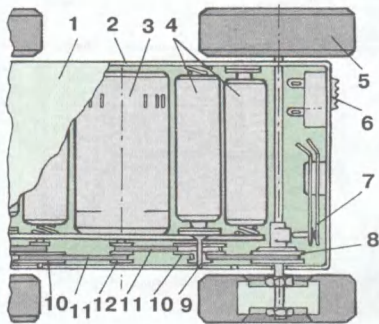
Механический блок модели: 1 — крышка; 2 — корпус; 3 — электромотор; 4 — батарея питания; 5 — ведущее колесо; 6 — выключатель; 7 — контактная пара прерывателя проблескового маяка; 8 — ведомый шкив; 9 — ось промежуточного шкива; 10 — промежуточный шкив; 11 — пазик; 12 — ведущий шкив двигателя.
